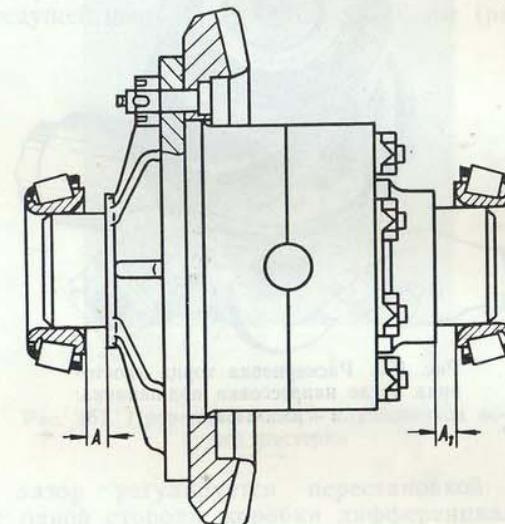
Зазоры A и A_1 между торцами подшипников и коробки сателлитов
